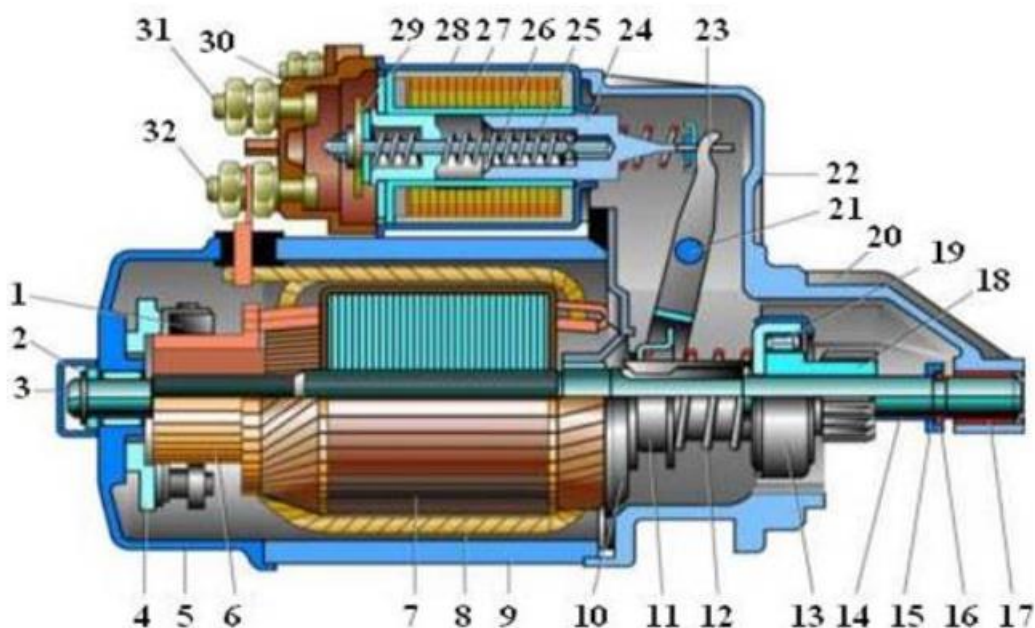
будова стартера: 1 – щітковий вузол; 2 – задня втулка; 3 – накривка втулки; 4 – тримач щіток; 5 – задня накривка корпусу стартера; 6 – щітковий колектор; 7 – якір; 8 – обмотка збудження; 9 – корпус (стакан); 10 – ізолююча шайба; 11 – втулка відведення; 12 – буферна пружина; 13 – муфта вільного ходу; 14 – вал якоря; 15 – упорна шайба; 16 – гумове кільце; 17 – втулка (підшипник ковзання) вала якоря; 18 – шестірня обгінної муфти (бендикс); 19 – ролики муфти вільного ходу; 20 – передня накривка корпусу стартера; 21 – валик важеля вмикання стартера; 22 – накривка тягового реле; 23 – важіль вмикання стартера; 24 – якір тягового реле; 25 – пружина; 26 – шток; 27 – котушка тягового реле; 28 – корпус тягового реле; 29 – контактний диск; 30 – пластмасова накривка тягового реле; 31, 32 – контактні гвинти.
